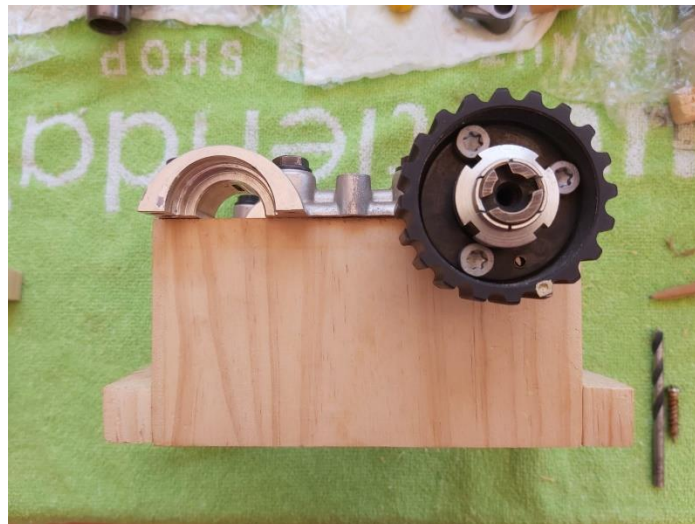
Vista frontal del ensamblaje de sujeción superior de los árboles de levas, estructura y eje 1 con piñón. Fuente: Propia
